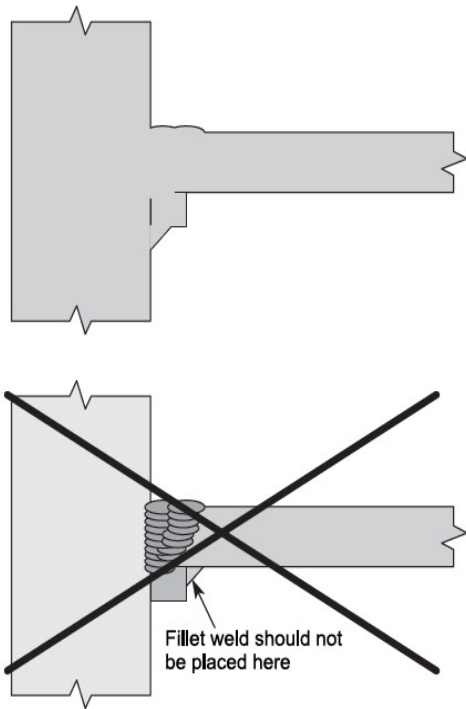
Marca con "x" el lugar donde no debe ir la soldadura de filete.
